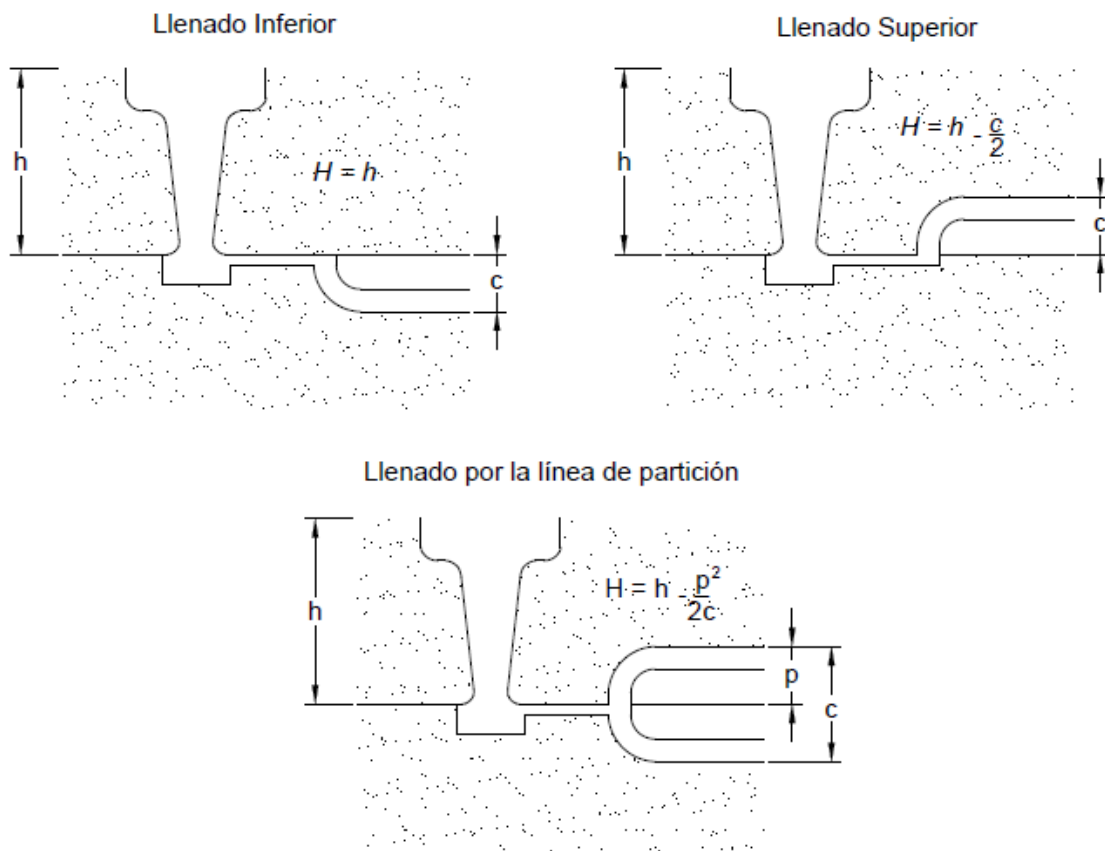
Disposición de diferentes tipos de llenado del molde.
